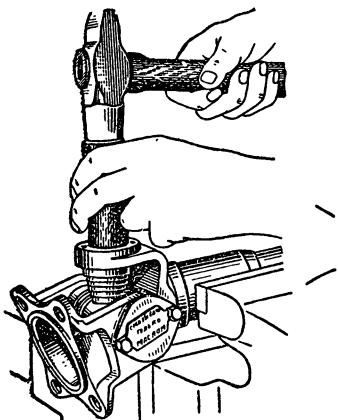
Выпрессовка подшипников из вилок карданного вала
